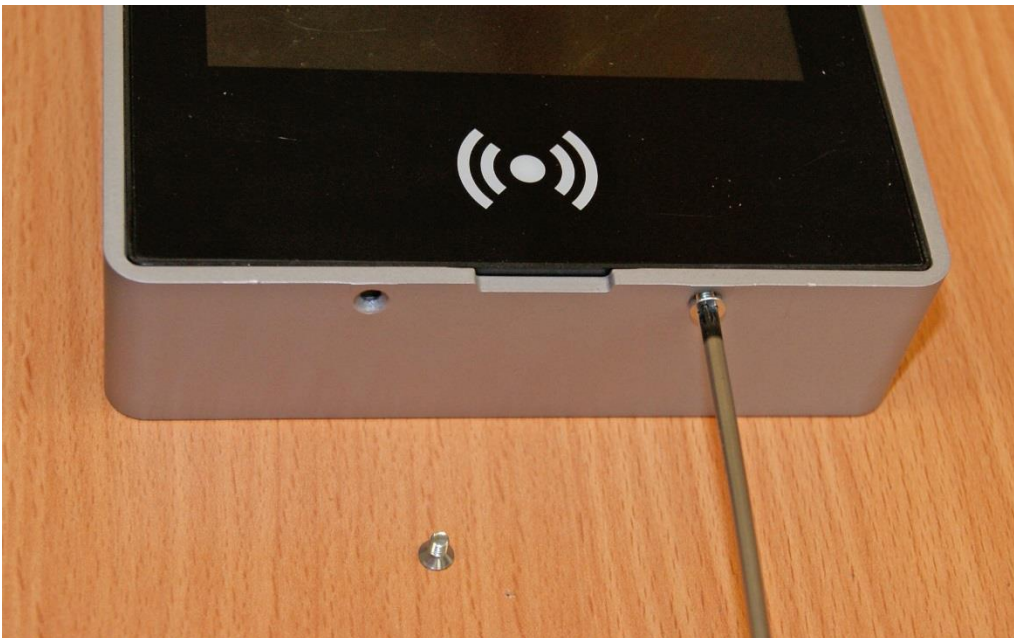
Entfernen der Schraube unten im Einbaurahmen
